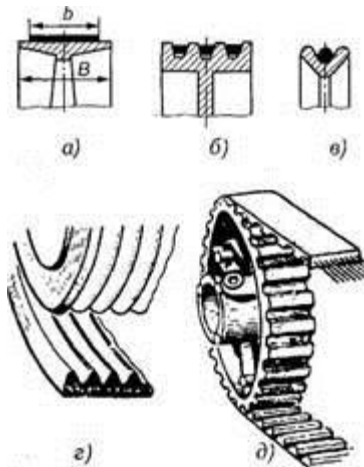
Типы ремней ременных передач: а — плоский ремень; б — клиновый ремень; в — круглый ремень; г — поликлиновый ремень; д — зубчатый ремень
